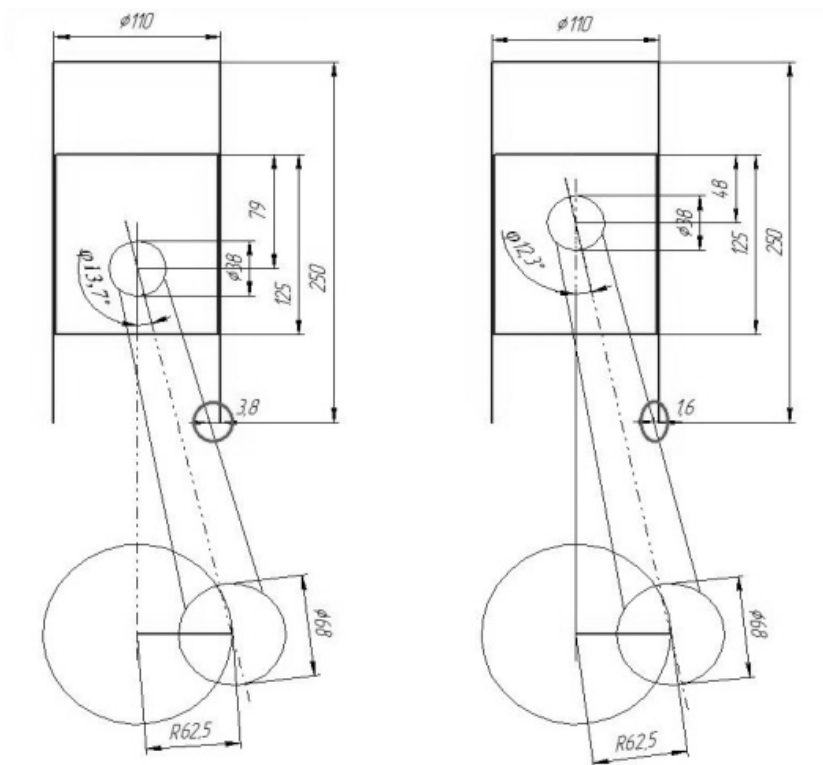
Положение деталей кривошипно-шатунного механизма двигателя Д-245 и их размеры
